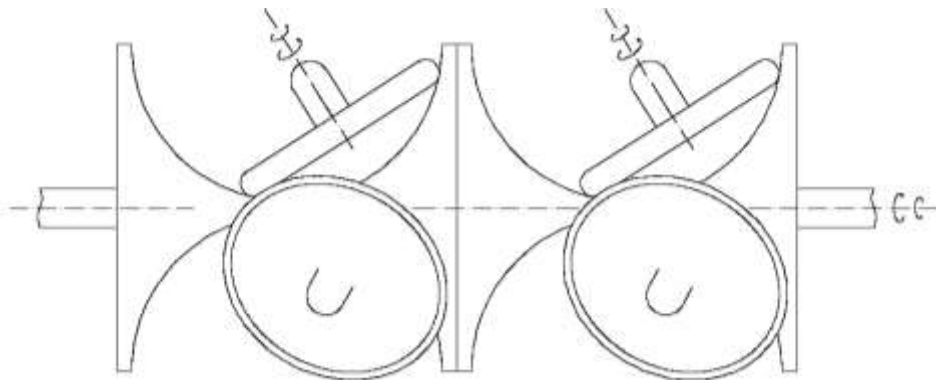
Тороидальный двухступенчатый вариатор с тремя промежуточными дисками в каждой ступени
